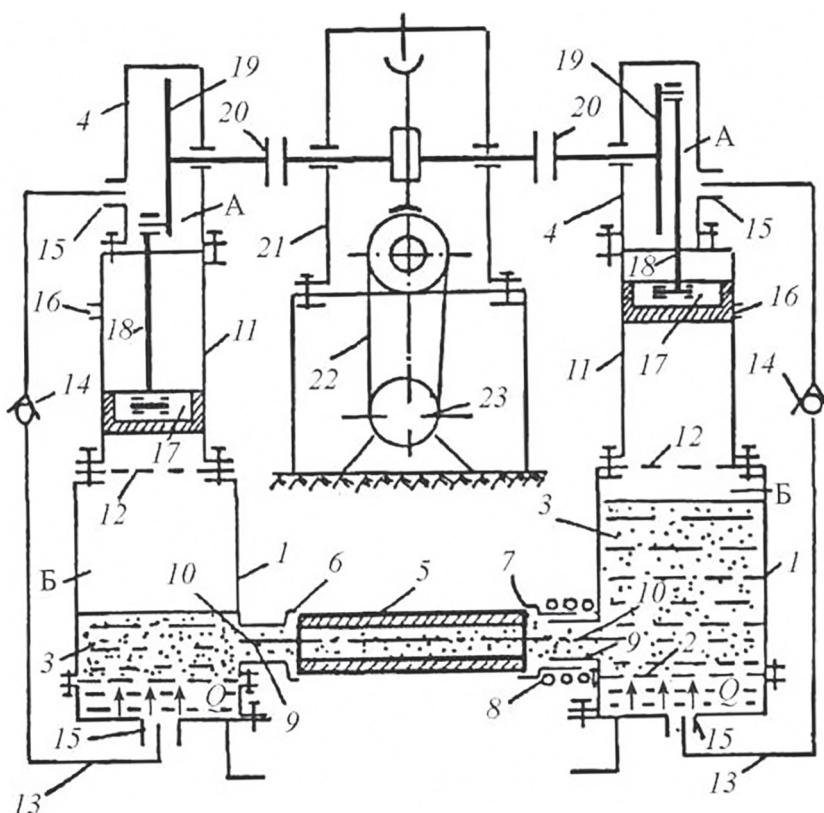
Схема устройства для гидроабразивной обработки внутренней поверхности труб:
